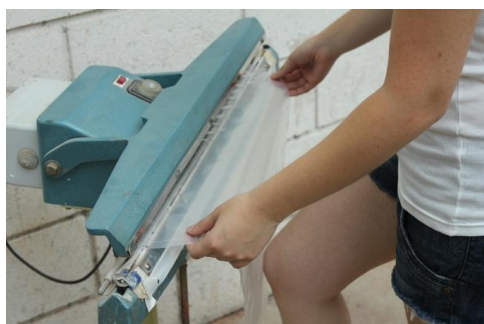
Fabricación y soldadura de las bolsas
